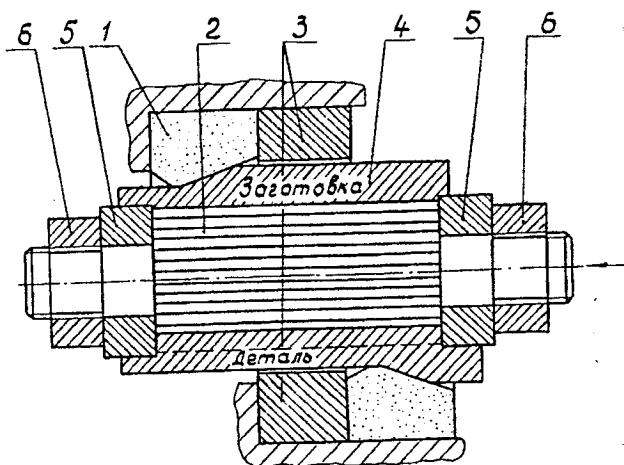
Схема редукування трубної заготовки на шліцьовій оправці з обмеженням осьової течії металу:
